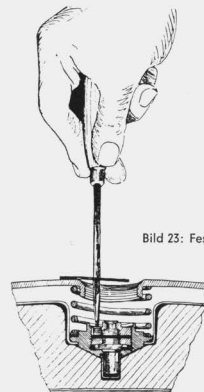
Festschrauben des Gewindestiftes der Einstellschraube
